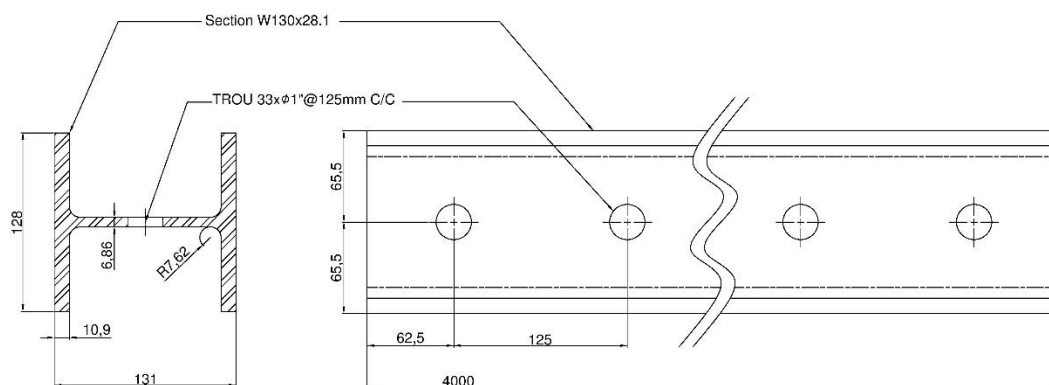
Plan d'usinage de la poutre pour essais préliminaires
